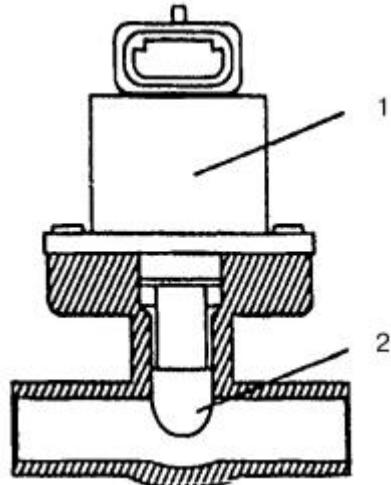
Дозатор (аттуатор): 1 – шаговый двигатель; 2 – шток.
